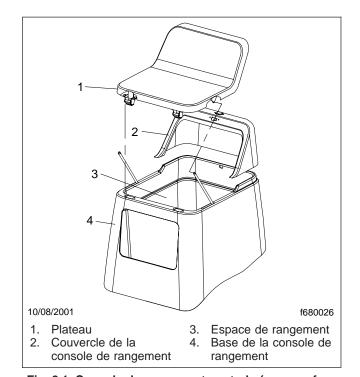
, Console de rangement centrale (avec surface d'écriture)
